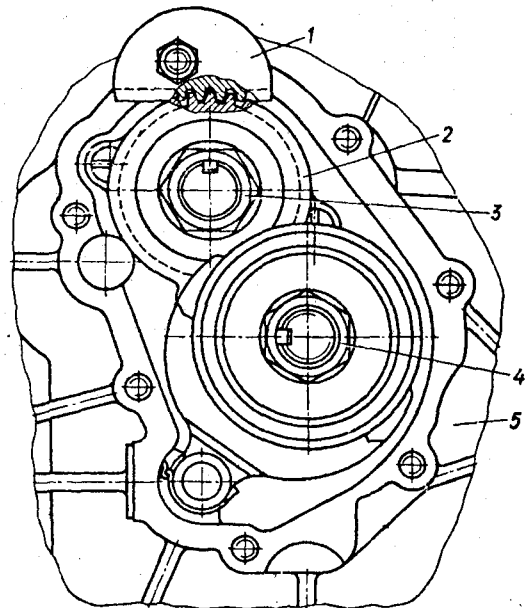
Стопорение пятой передачи коробки передач при отворачивании и заворачивании гаек ведущего и ведомого валов: 1 – стопор; 2 – шестерня ведущая пятой передачи; 3, 4 – гайка ведущего и ведомого валов; 5 – картер коробки передач
